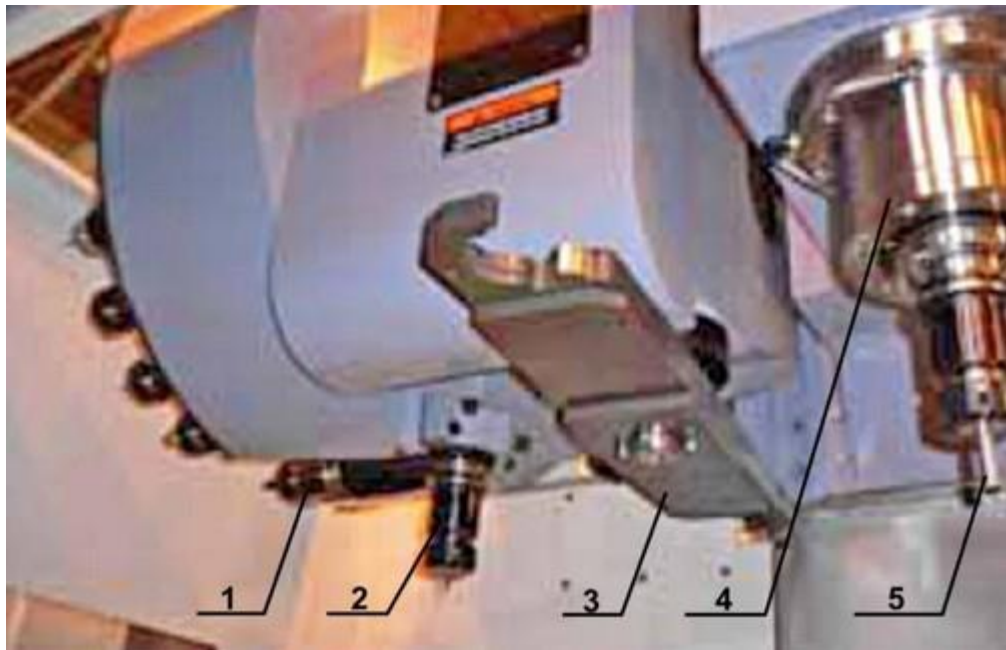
Процес зміни інструменту: 1 - інструмент в магазині у штатному положенні; 2 - інструмент на підготовчій позиції; 3 - маніпулятор у штатному положенні; 4 – шпиндель; 5 – інструмент у шпинделі
